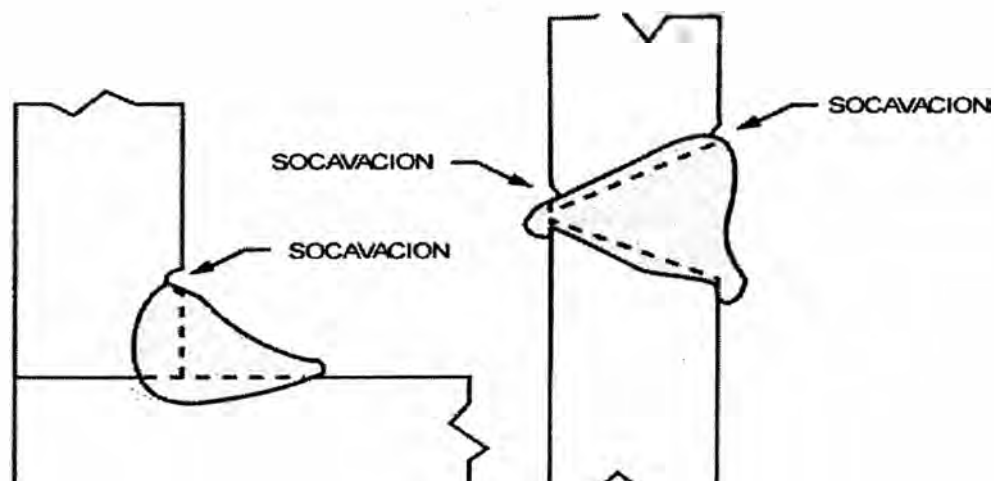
Apariencia típica de una socavación en soldaduras con bisel y de filete
